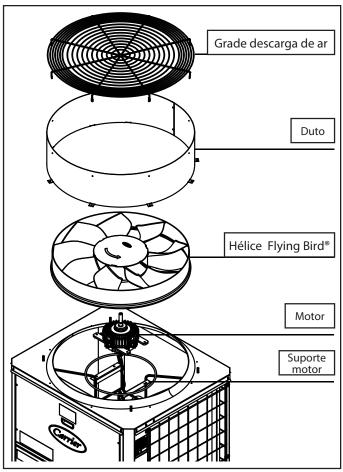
Vista explodida conjunto ventilador das un. condensadora 38EX/38EV e Hélice Flying Bird®
